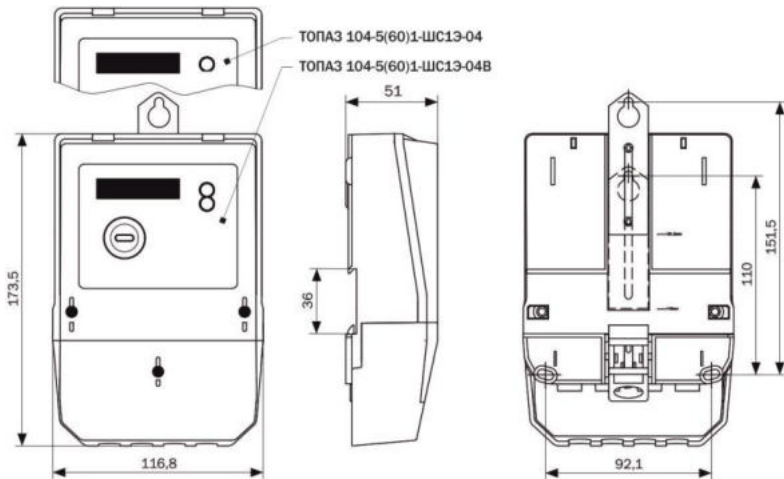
Внешний вид и присоединительные размеры счетчика однофазного ТОПАЗ 104
